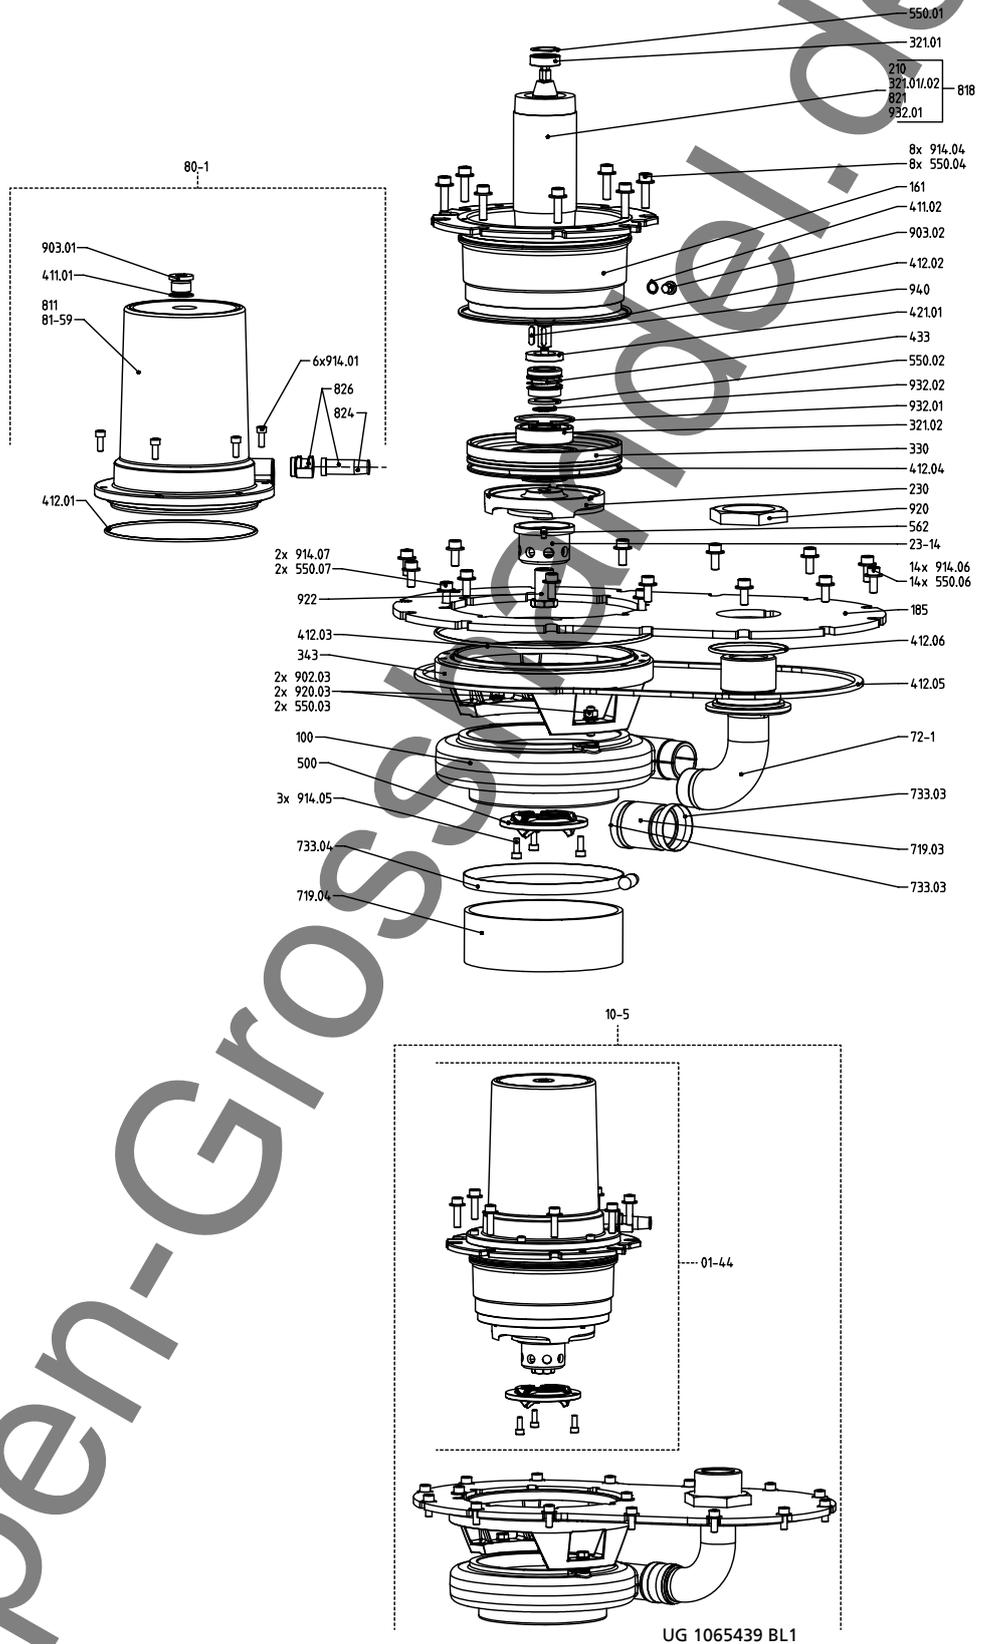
Explosionsdarstellung US100, UZS150 - Laufteil
